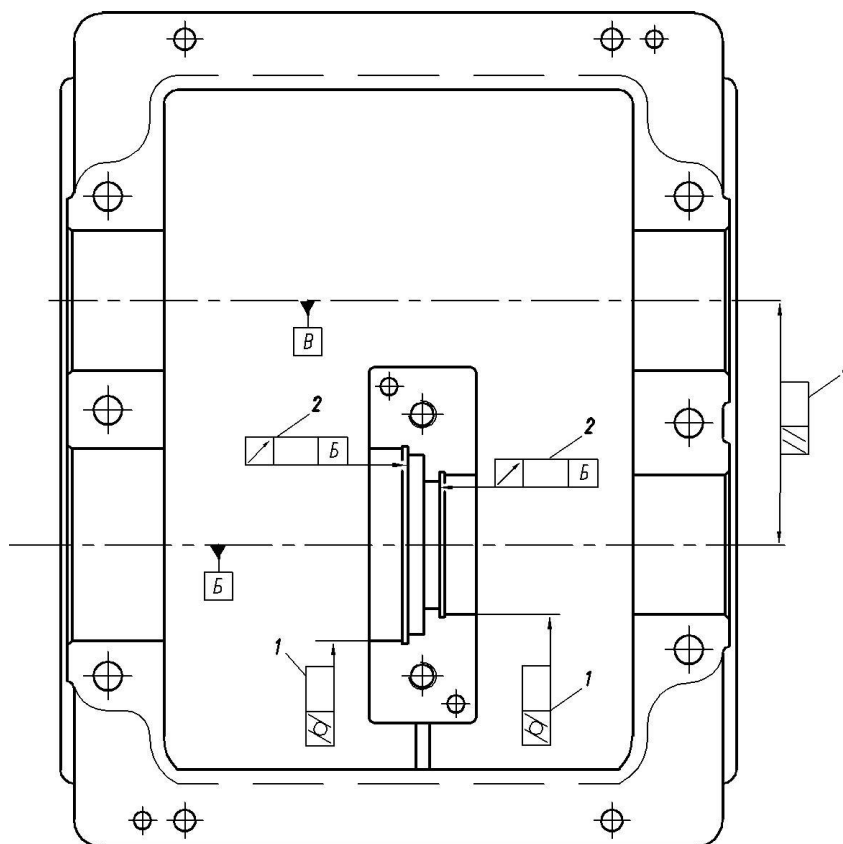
Размещение обозначений допусков форм и расположения поверхностей на чертеже основания корпуса соосного редуктора
